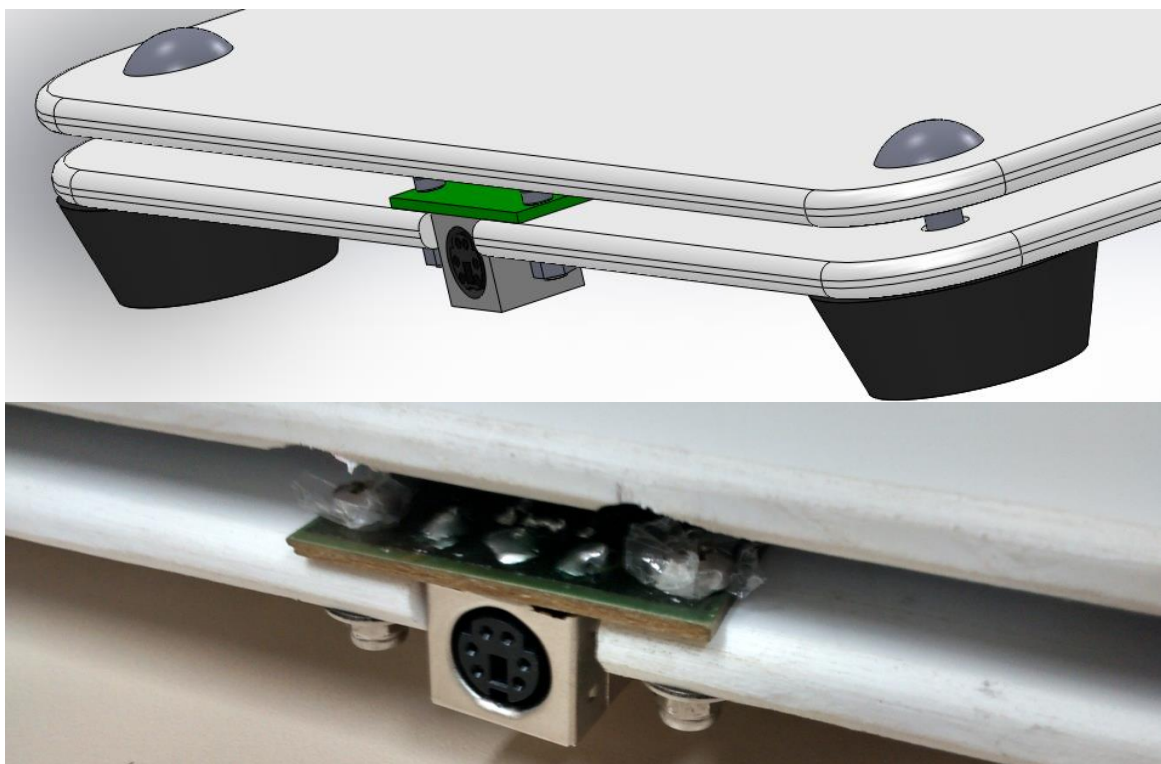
Fixação da PCB de conexão das plataformas e pés de borracha.
